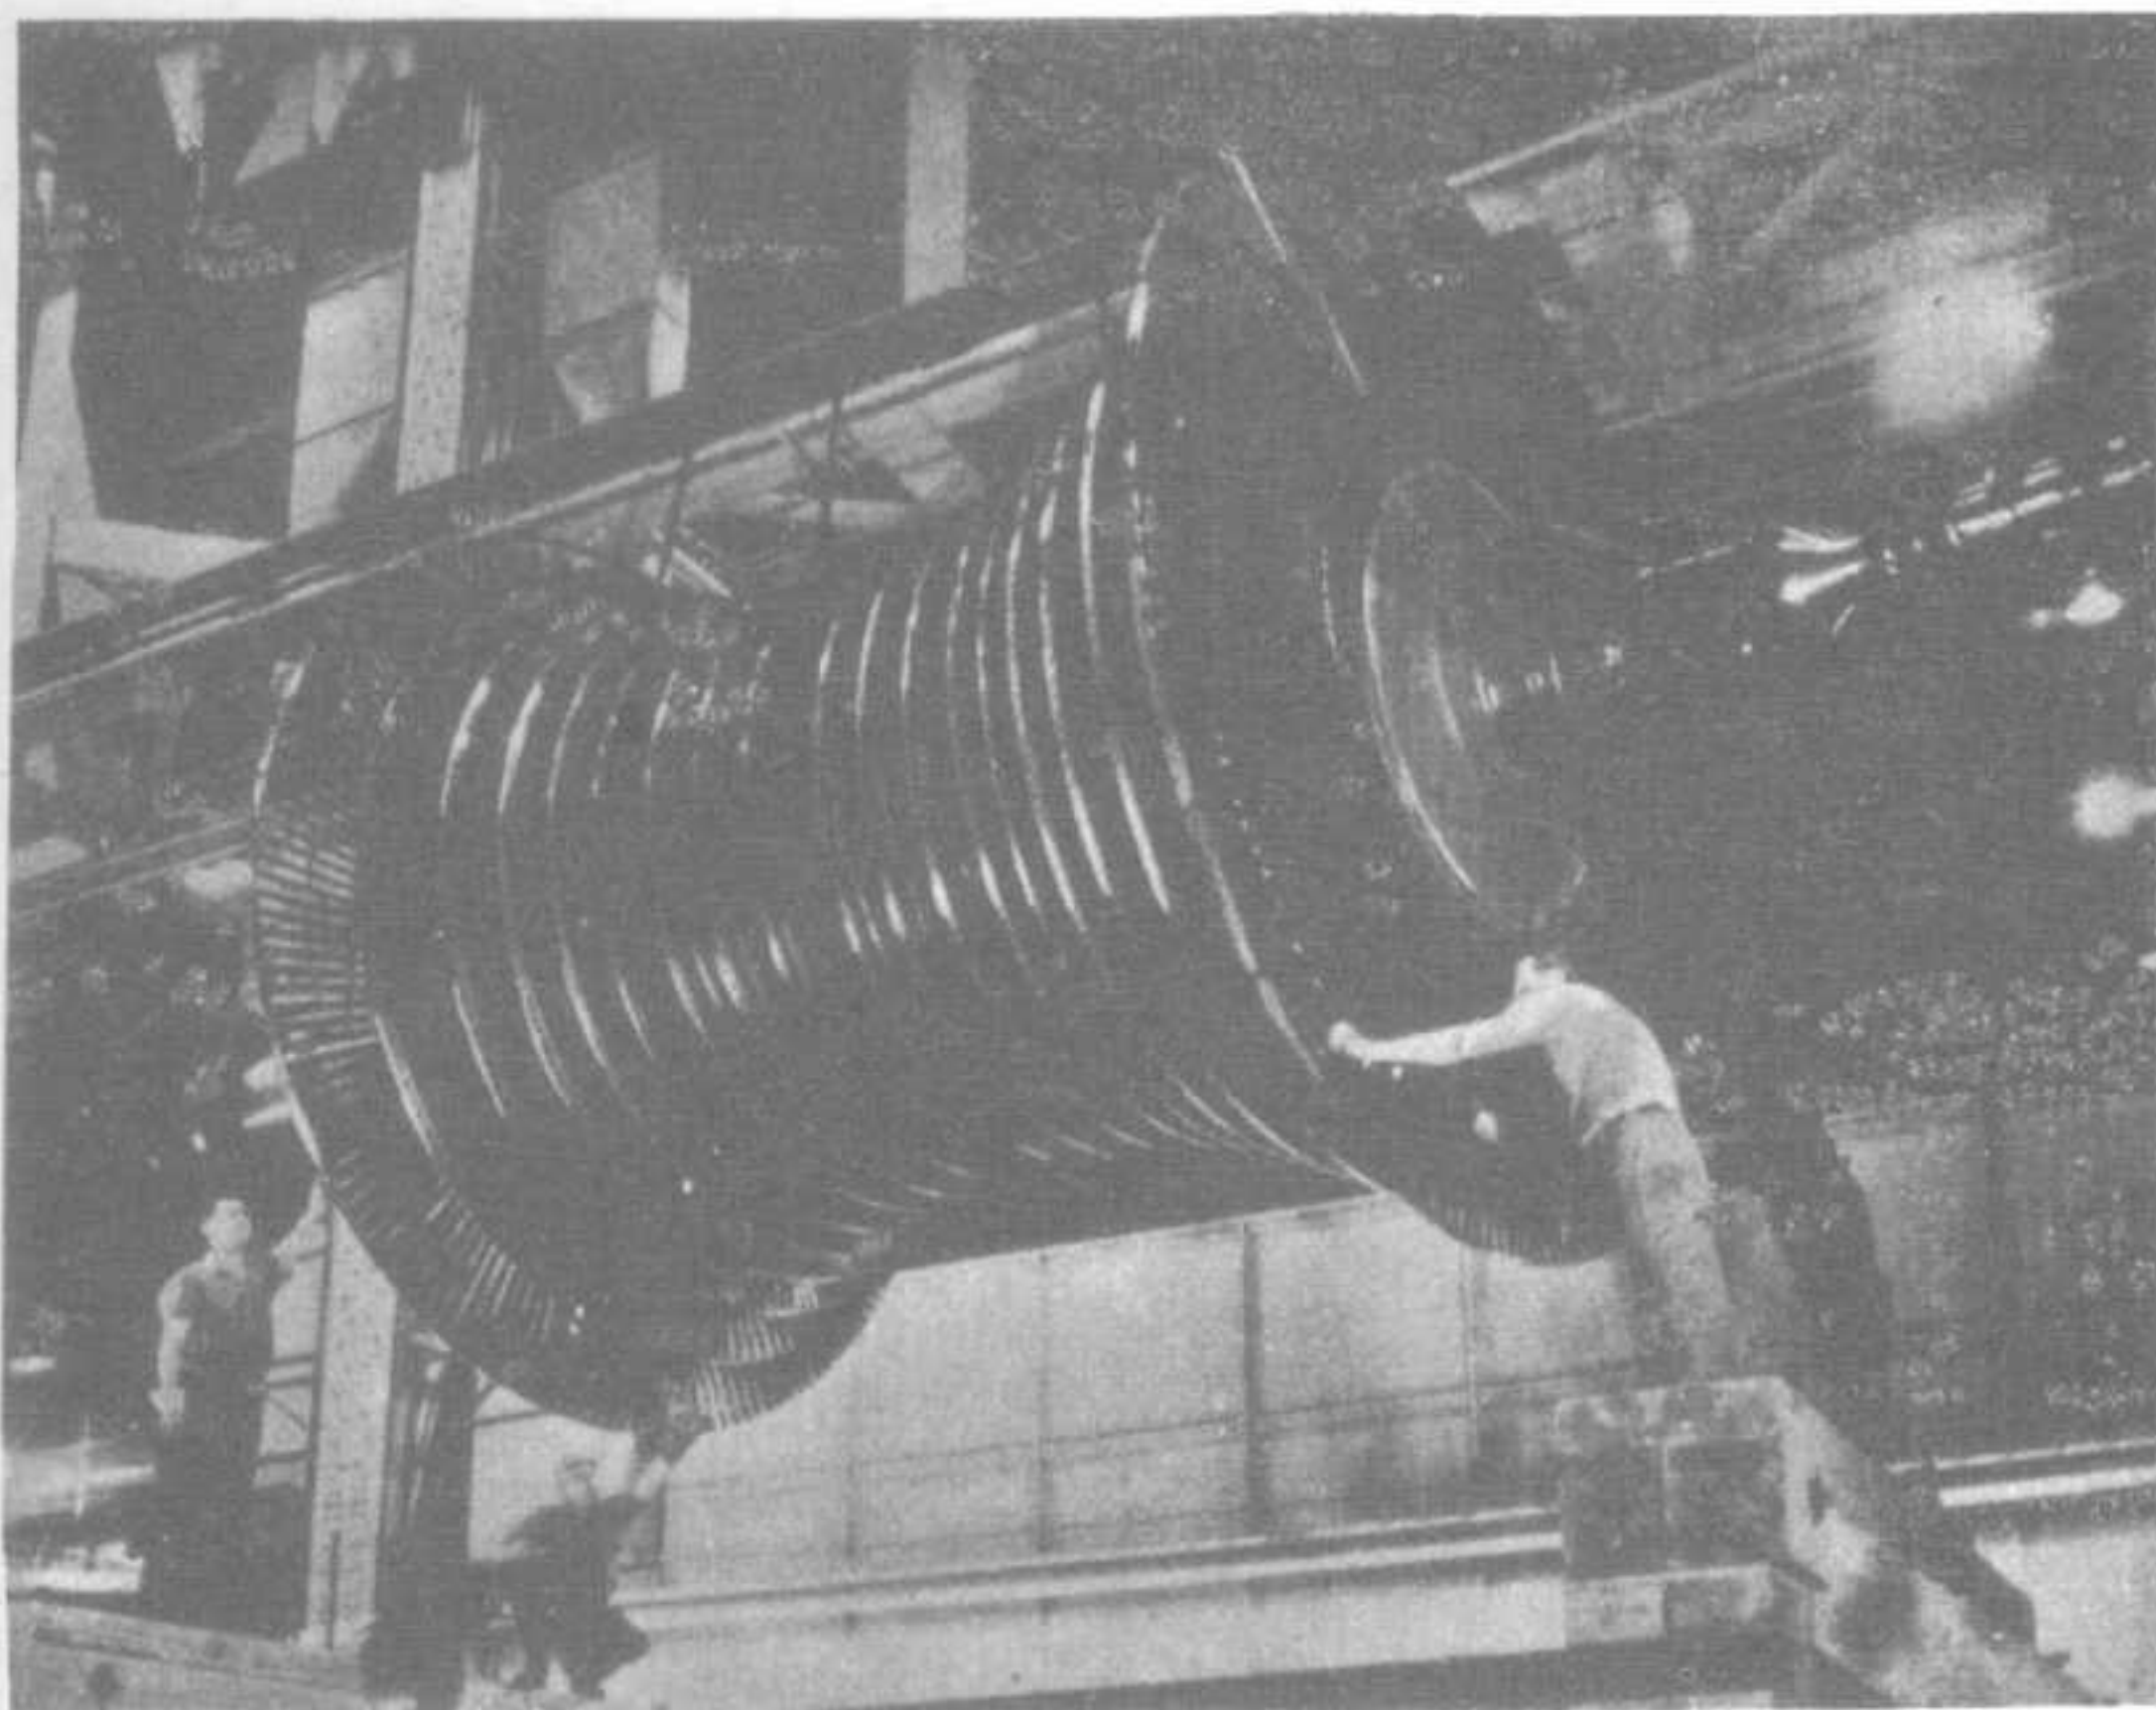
Rotor de turbina de vapor de doble flujo.
